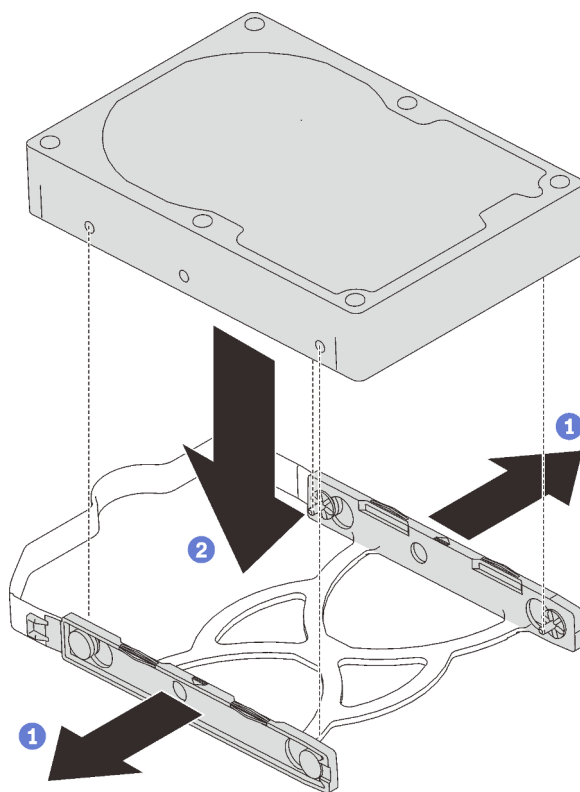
Installation d'une unité 3,5 pouces dans le dispositif de retenue
